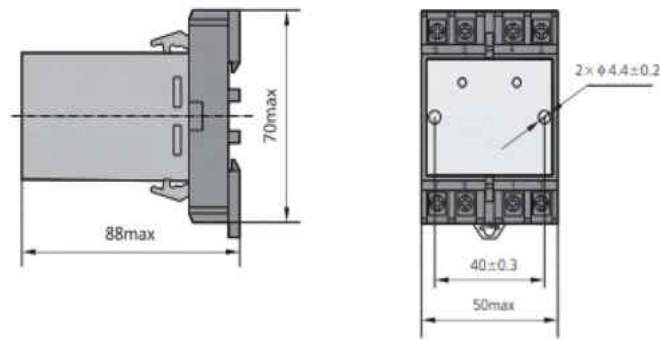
Dimensions et Montage de CHINT JYB-714C [3]
